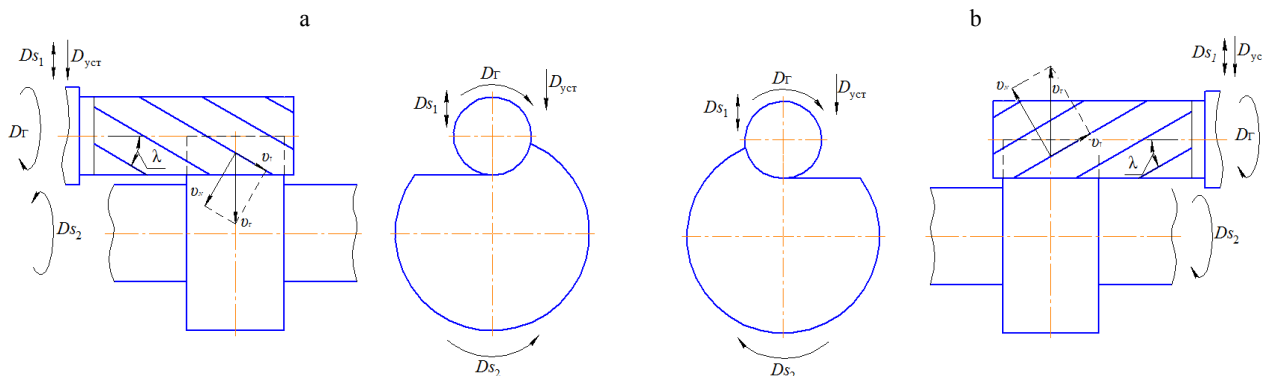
Схемы обработки плоской поверхности детали при попутном (а) и встречном (б) фрезеровании
